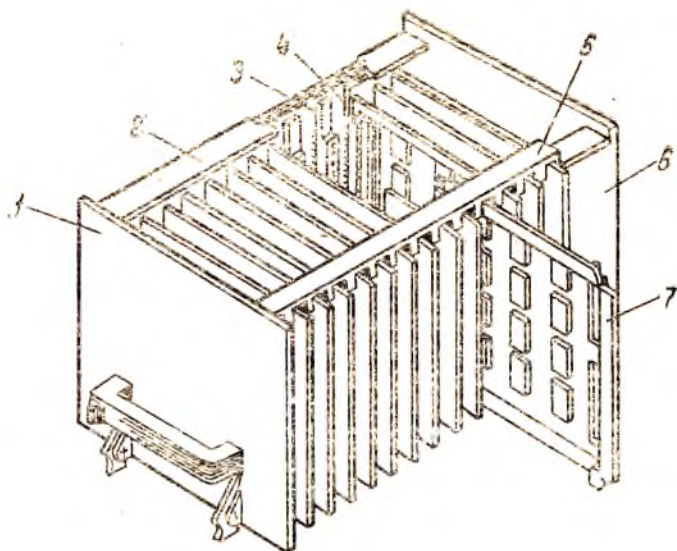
Блок разъемного типа самолетной МЭА: 1—передняя панель; 2 — угольник; 3 — розетка соединителя РППМ26; 4 — объединительная плата; 5 — направляющая; 6 — задняя панель; 7 — ячейка с выключной частью соединителя РППМ26
